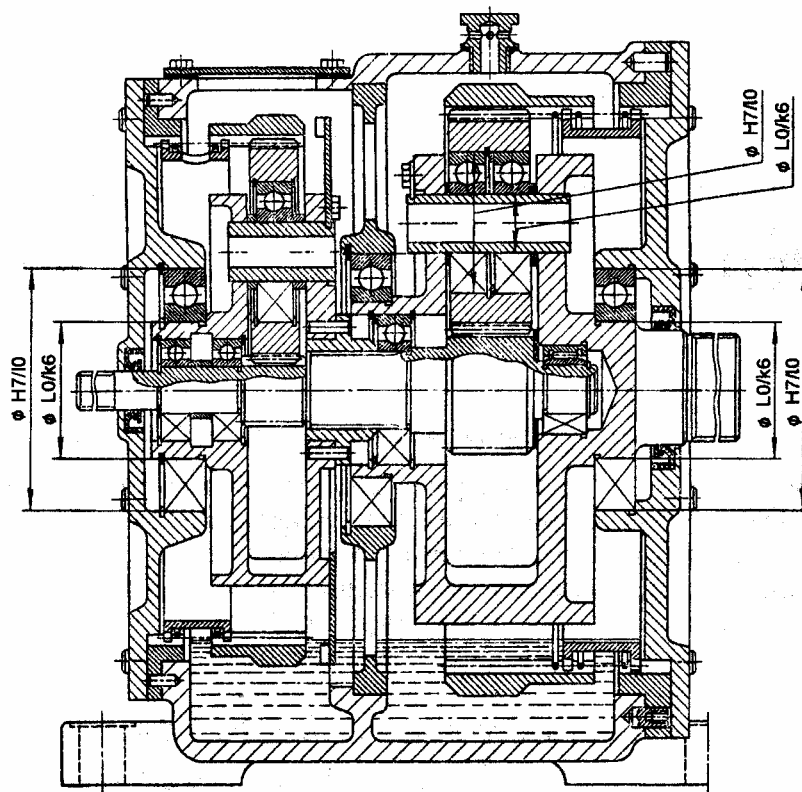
Планетарный однорядный двухступенчатый редуктор
